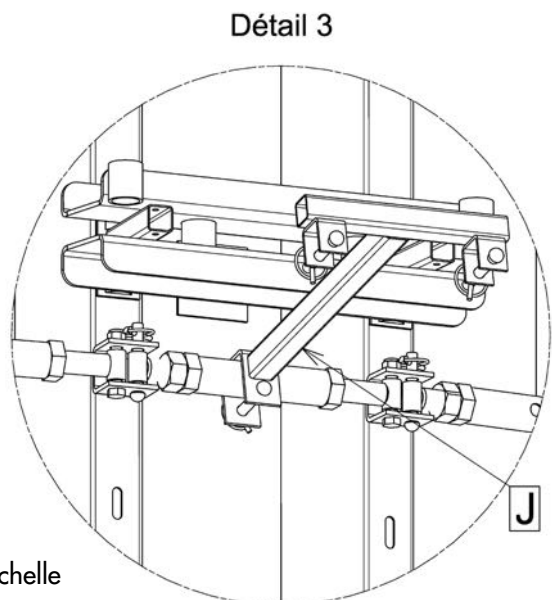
Détail 3 fixation de la fixation basse de l'échelle
